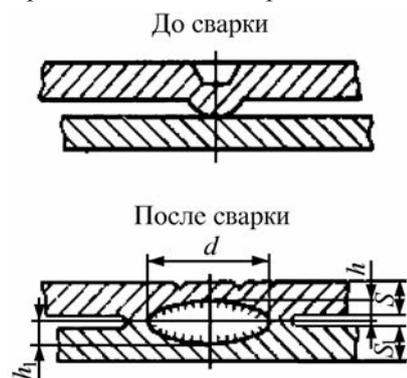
Конструктивные элементы сварных соединений, выполненных контактной рельефной сваркой: S и $S1$ — толщина частей детали; d — расчетный диаметр литого ядра точки или ширина литой зоны шва; h и $h1$ — глубина проплавления
